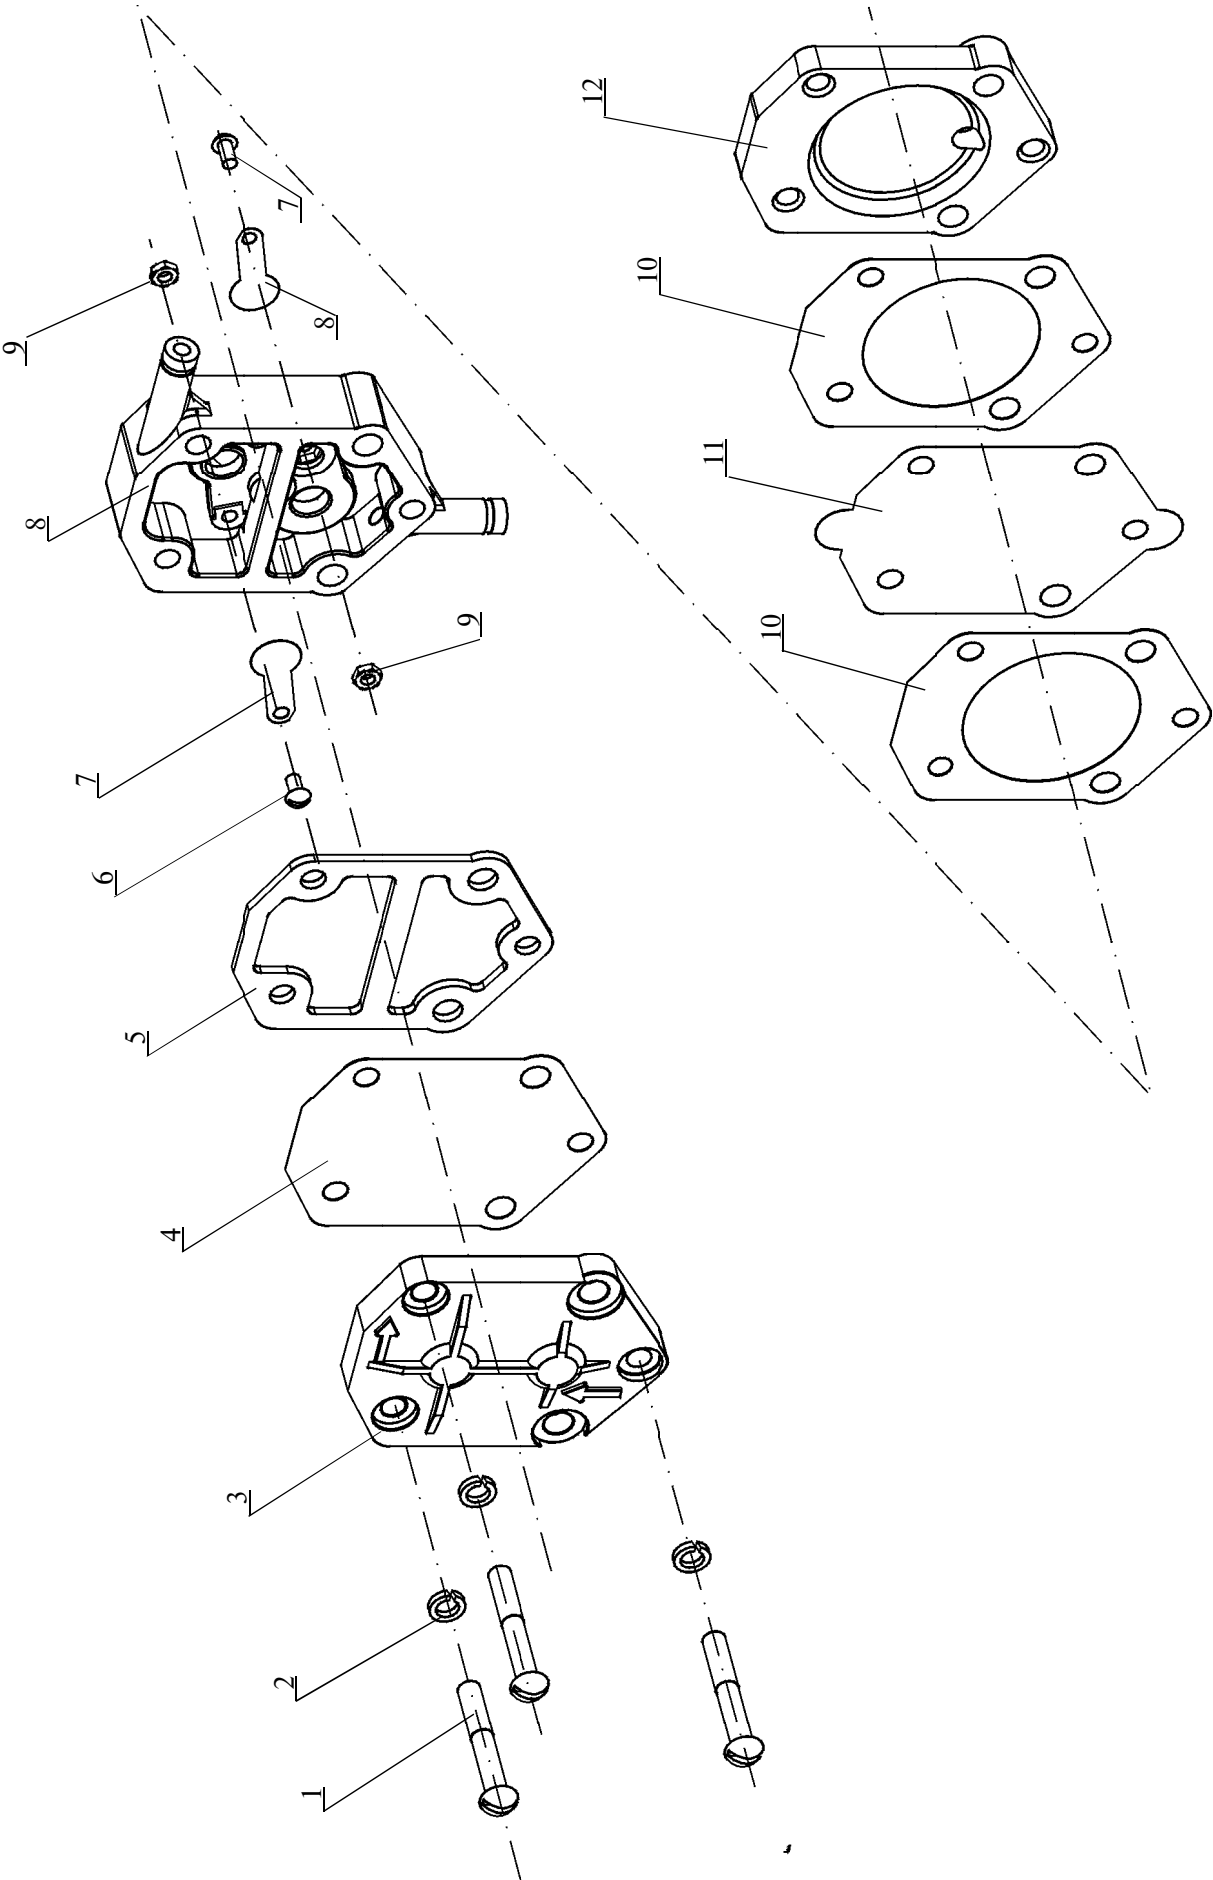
0584906070 Топливный насос двигателя
